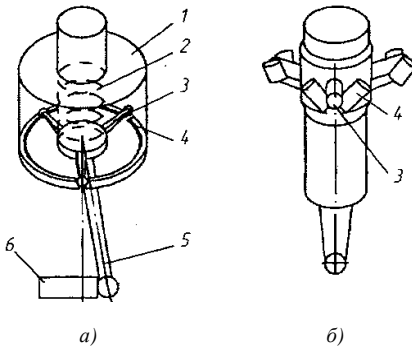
Схема устройства для контроля целостности сверла по касанию детали
